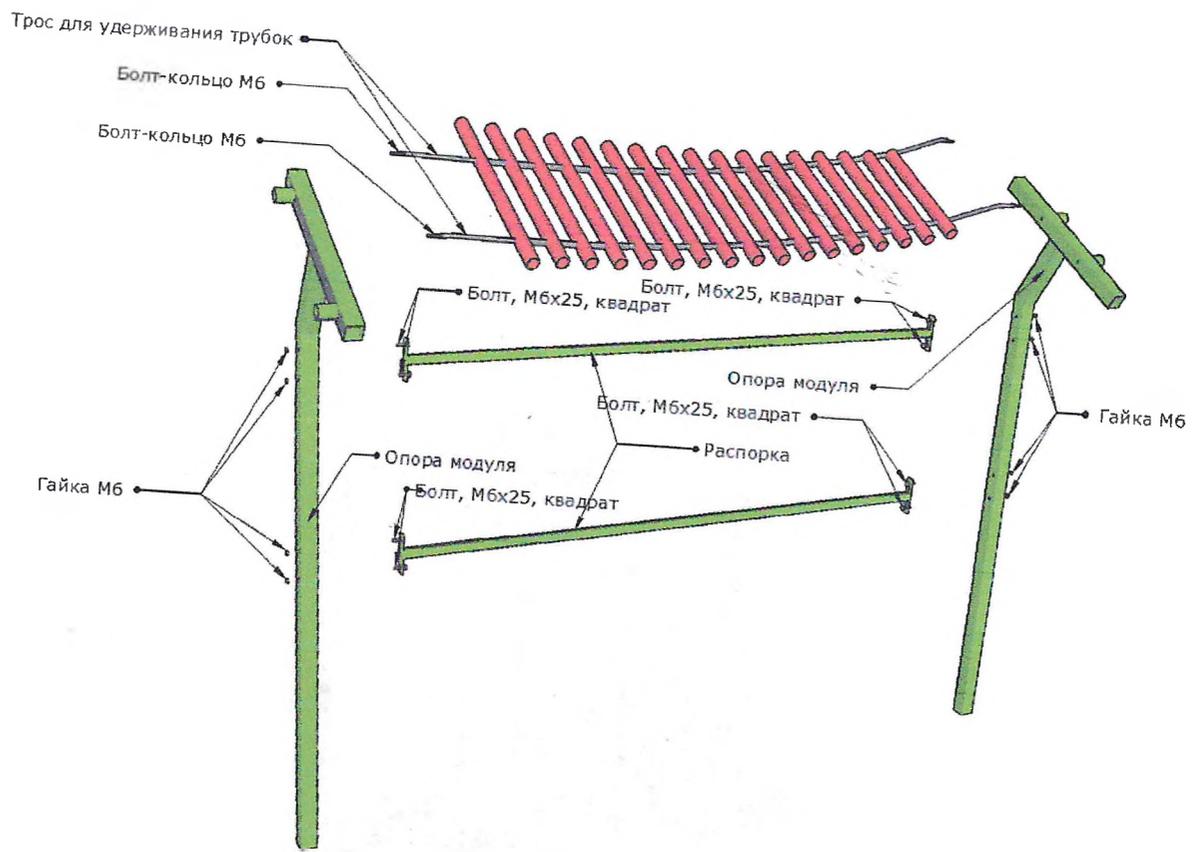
схема расположения деталей металлофона «Веселая песенка»
